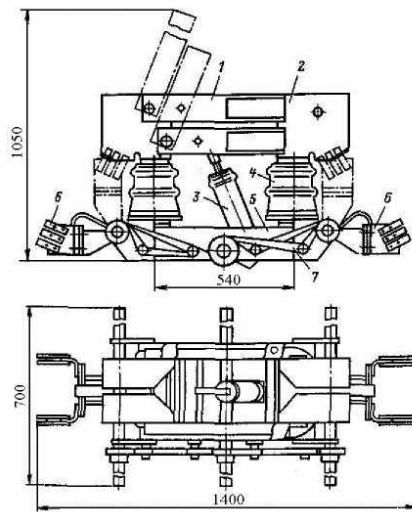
Роз’єднувач рубаячого типу для внутрішньої установки з двома заземлюючими ножами РВРЗ-2-20/8000 [1]: 1 – головні рухомі контакти; 2 – нерухомі контакти; 3 – фарфорова тяга; 4 – опорний ізолятор; 5 – рама; 6 – заземлюючі ножі; 7 – блокування
